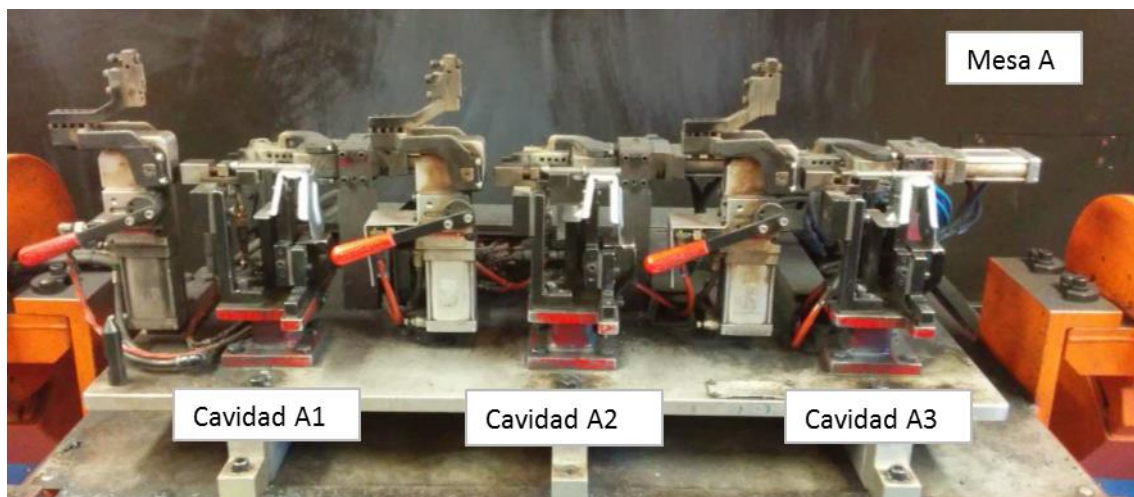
Fotografía de las 3 cavidades de la mesa A del útil de soldadura. Imagen elaborada por el autor del TFM.
